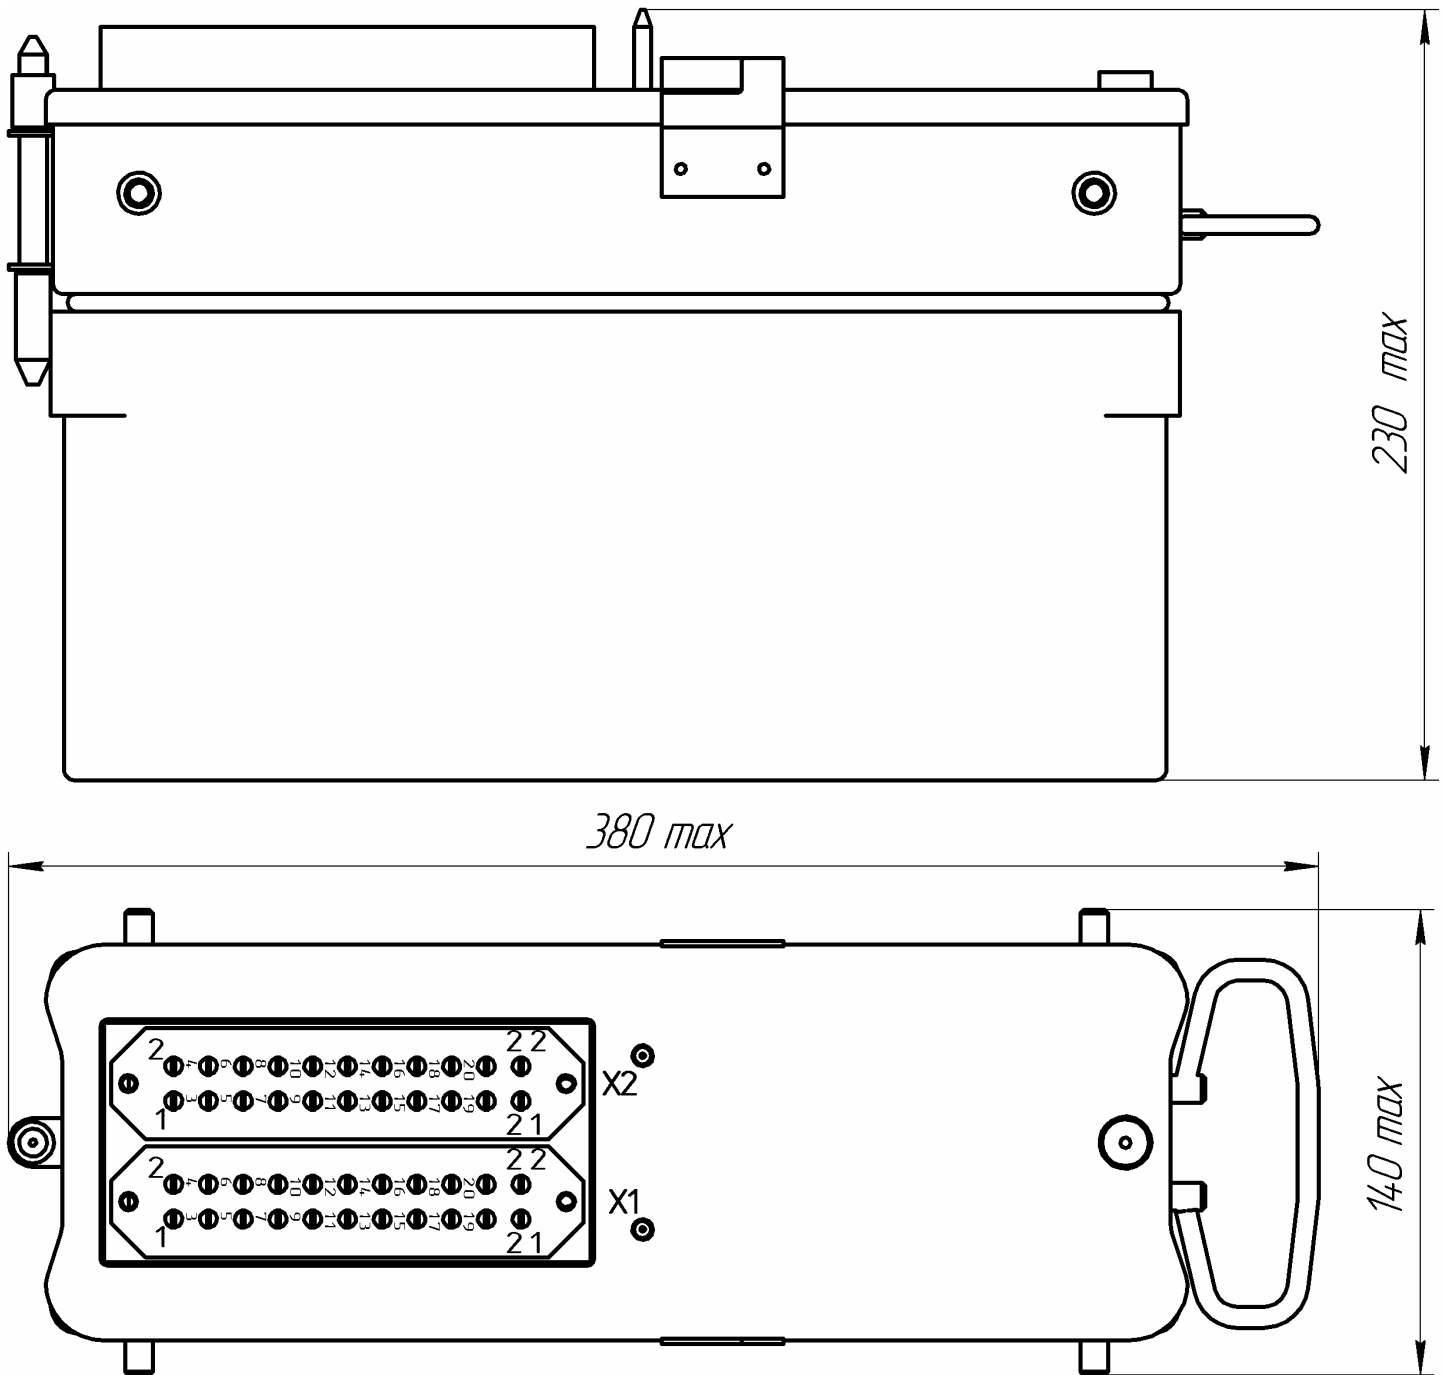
габаритные размеры блока БЗСГ-02М
